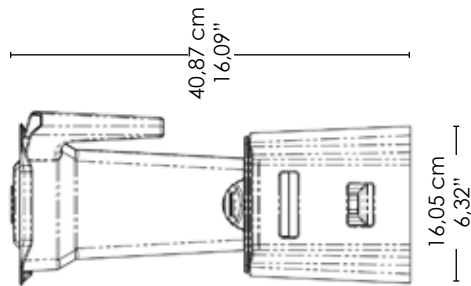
SUR LE PLAN DE TRAVAIL : SPACESAVER
